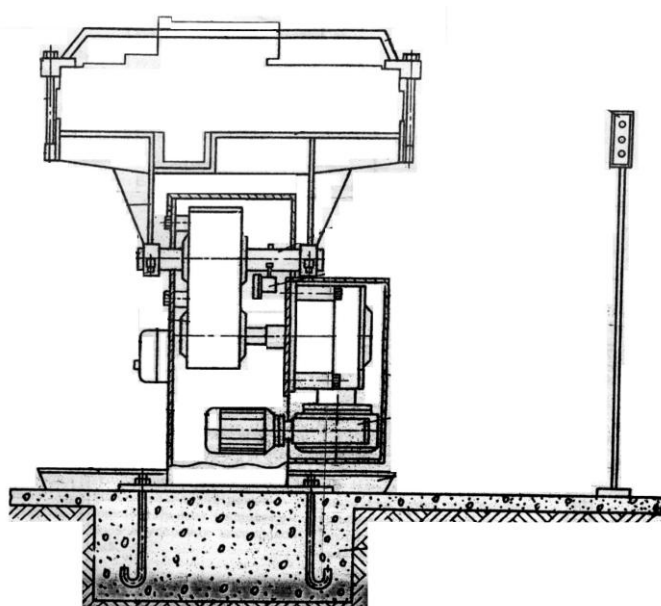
Крепление редуктора заднего моста для сборки и разборки
